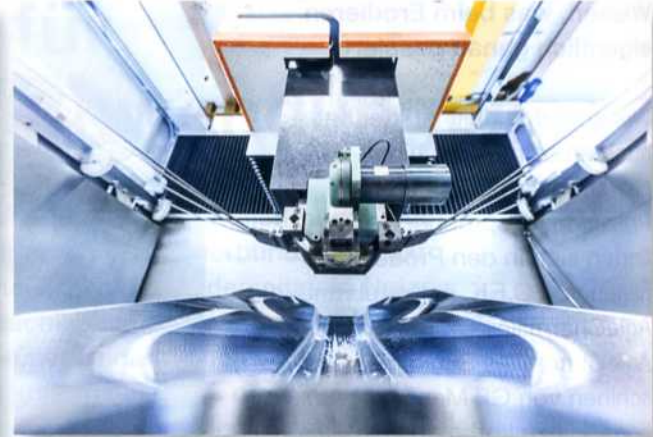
In dem Erodierzentrum steht die weltweit einzige AgieCharmilles Drahterodiermaschine AC Progress V4 von GF Machining Solutions mit 715 mm Schnitthöhe
